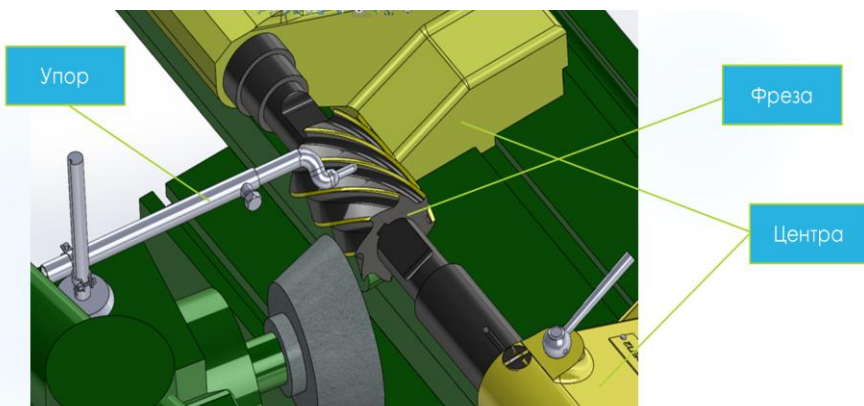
Наладка станка на заточку цилиндрической фрезы по винтовой задней поверхности
